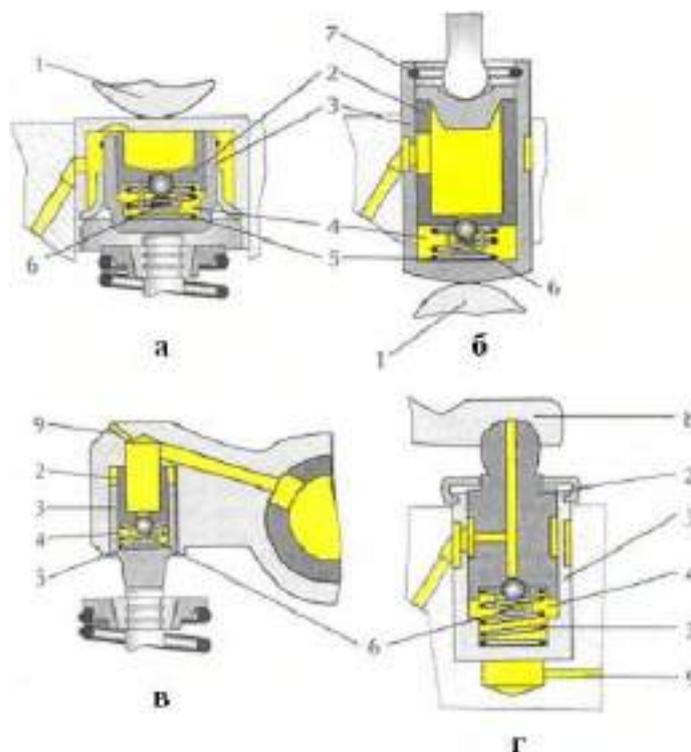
Устройство и расположение гидрокомпенсаторов: а – в толкателе с верхним рас- предвалом; б – в толкателе с нижним распределвалом; в – в коромысле; г – в опоре рычага привода кла- пана ГРМ; 1 – кулачок; 2 – плунжер; 3 – втулка плунжера; 4 – полость под плунжером; 5 – пружина плунжера; 6 – пружина шарикового клапана; 7 – стопорное кольцо; 8 – рычаг привода клапана; 9 – дренажное отверстие
